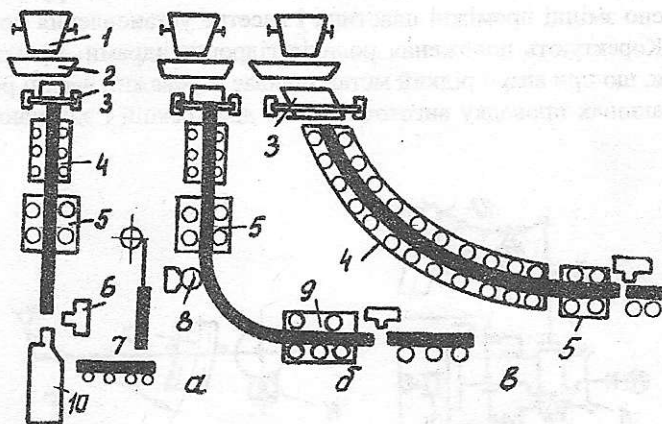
Схема вертикальної (а), зі згином злитка (б) і радіальної (в) машин неперервного лиття: 1-розливний ківш; 2-проміжний ківш; 3-кристалізатор; 4-зона вторинного охолодження; 5-тягнуча кліть; 6-газоріз; 7-рольганг; 8-згибний пристрій; 9-прямильний пристрій; 10-кантувач
